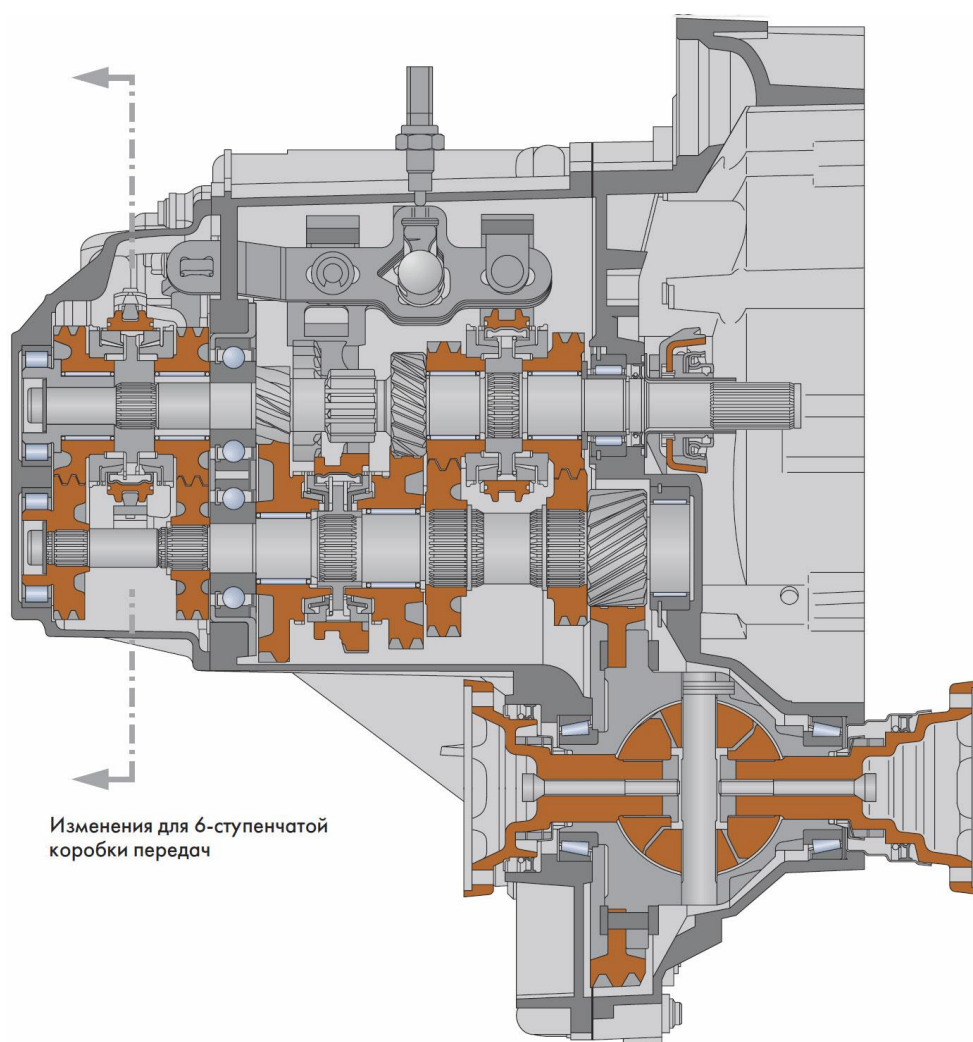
Механическая 6-ти ступенчатая коробка передач VW.
